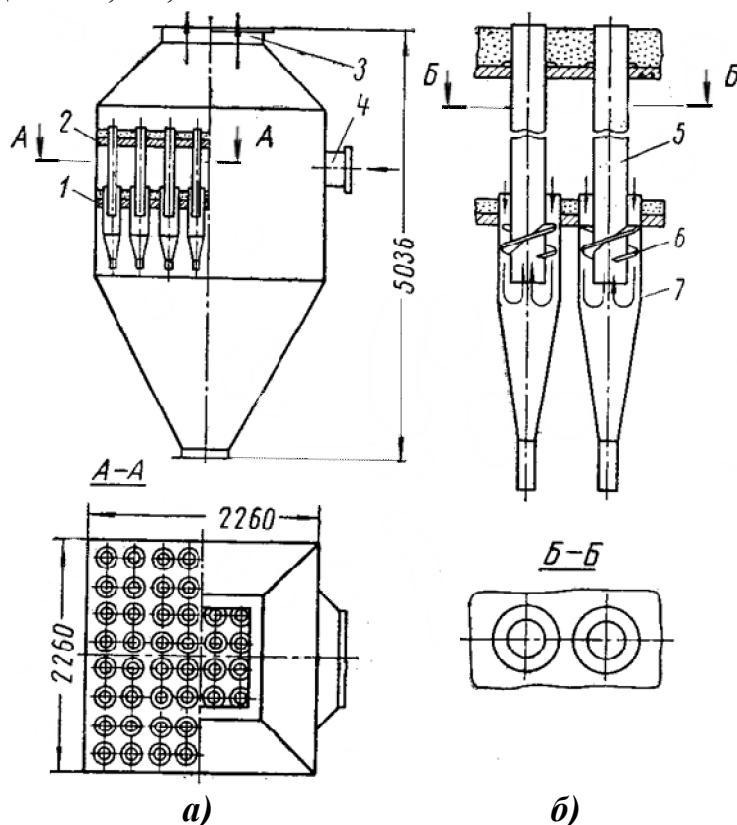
Схема батарейного циклона: а – циклон; б – элементы циклона; 1, 2 – решетки для крепления элементов циклона; 3 – штуцер для выхода очищенного газа; 4 – штуцер для входа запыленного газа; 5 – труба для выхода газа; 6 – винтовая направляющая для потока газа; 7 – корпус элемента циклона
